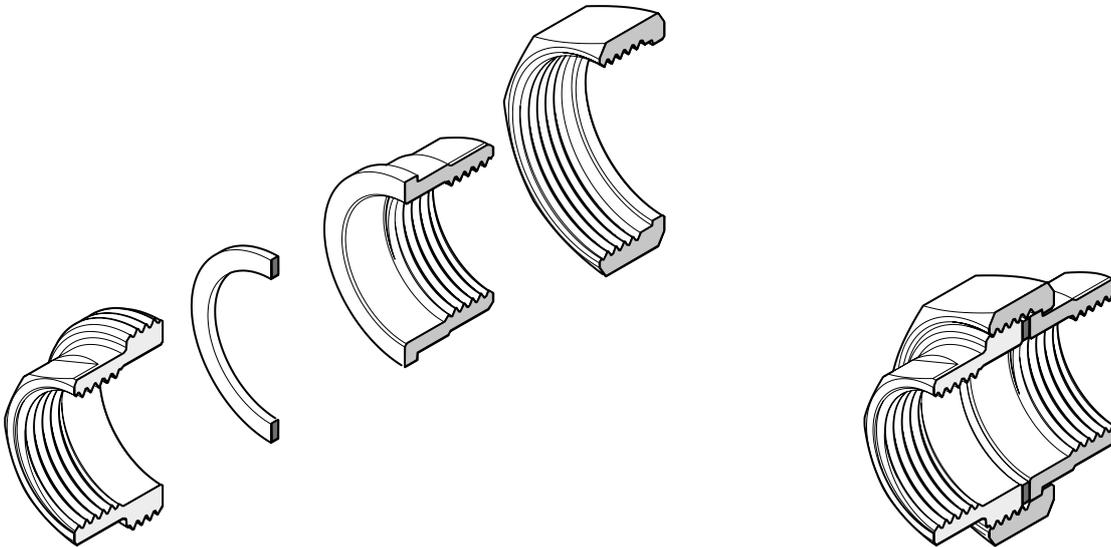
Assemblage par filetage de tuyaux selon ISO 228-1 (non vissé/vissé)
